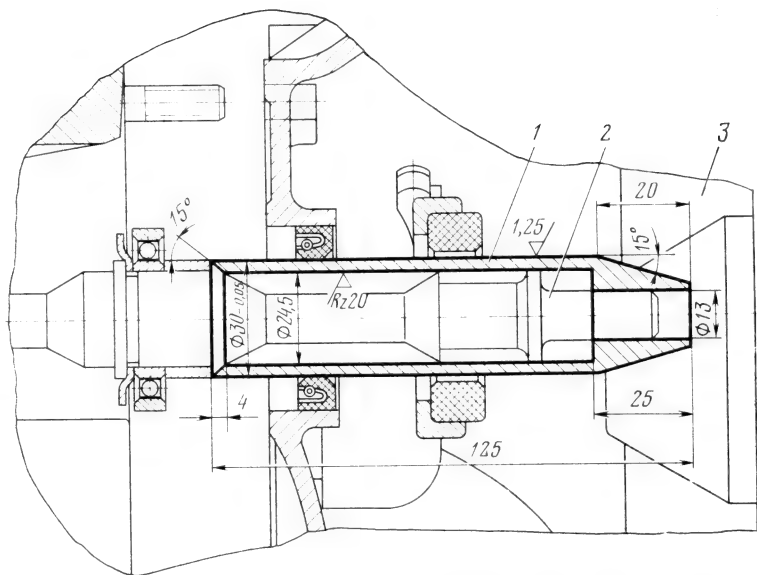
Оправка для установки картера сцепления в сборе с манжетой на картер коробки передач:
